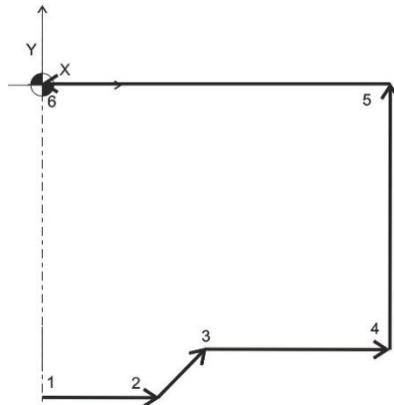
Koordinatenursprung bei einem Schaftwerkzeug ohne Werkzeugaufnahme
